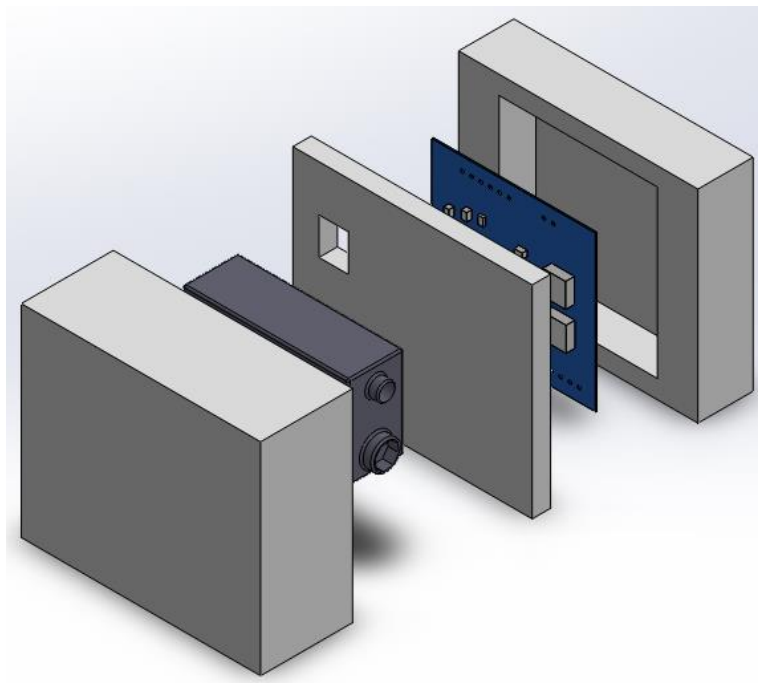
Vista explosionada del ensamble de la radiosonda.
